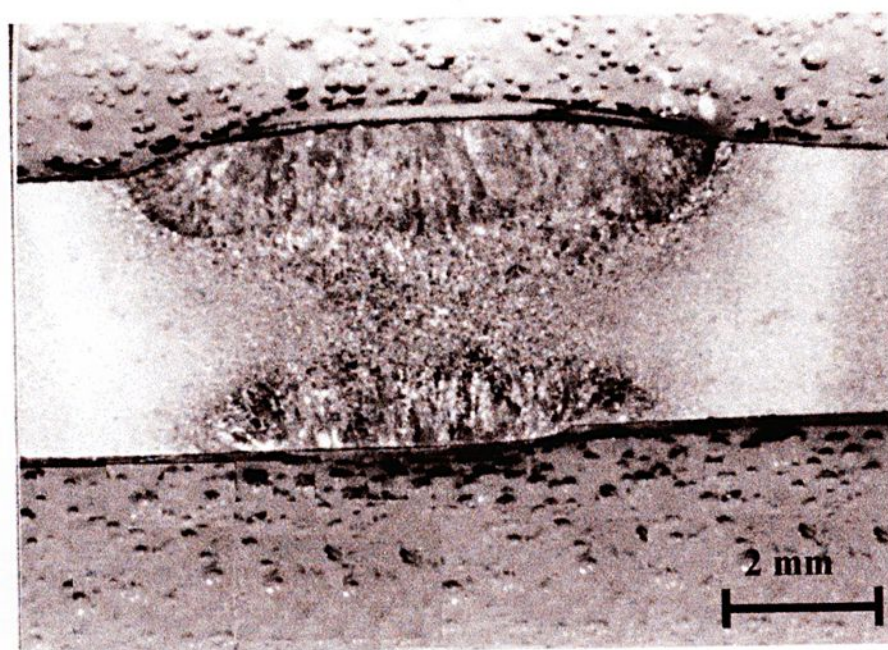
Cordão de solda da condição T0, onde pode-se notar os passes de soldagem, como na condição L0.
